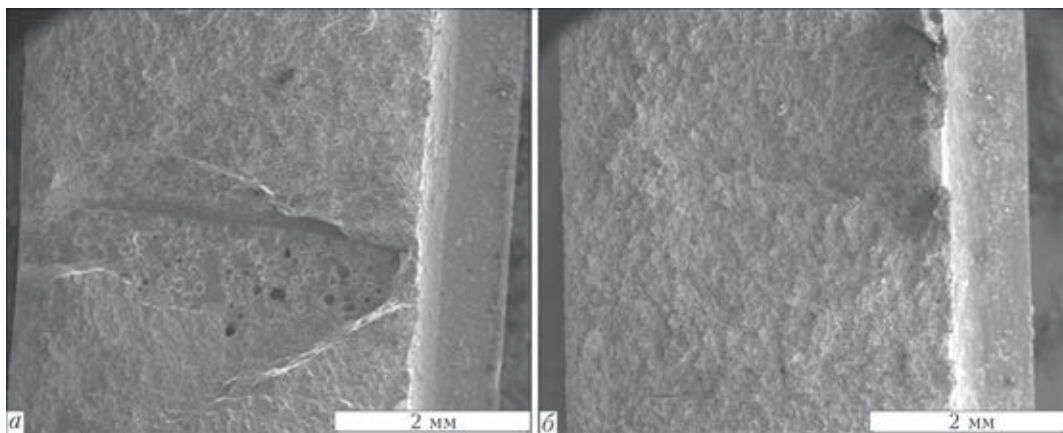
Макрофрактограммы поверхностей разрушений после испытаний на ударный изгиб: *a* — образец сварного соединения 1; *б* — образец 2 сварного соединения сплава технического титана BT1-0 ДШП толщиной 12, мм упрочненного азотом (0,098 мас. %)
